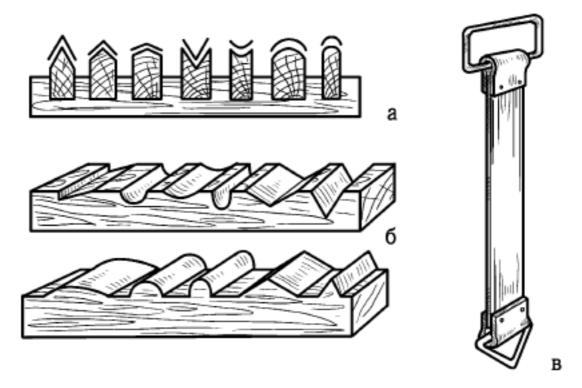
Приспособления для заточки и правки профильных стамесок: a — доска со вставленными профильными брусками и оселками;  $\delta$  — правочная доска с профилями стамесок;  $\epsilon$  — ремень
